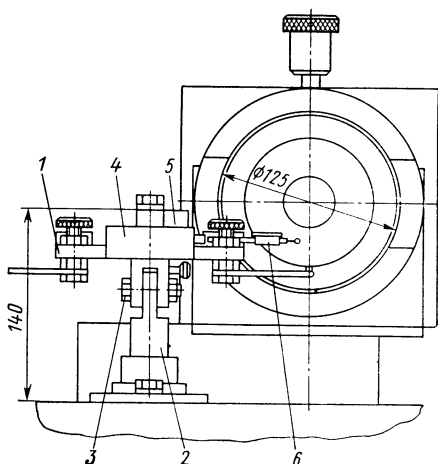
Приспособление для образования стружкозавивающих канавок на резцах
